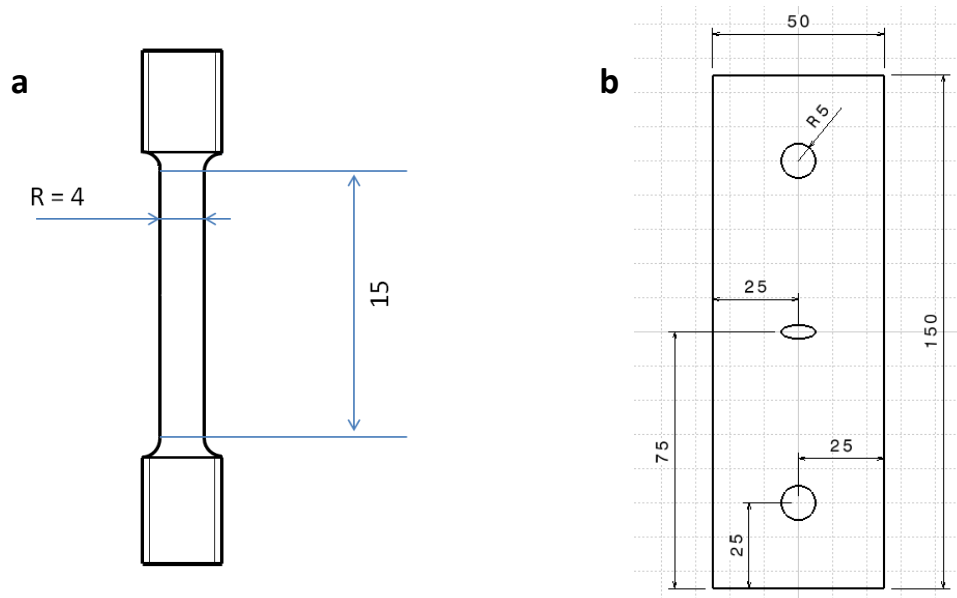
a) Schéma d’une éprouvette axisymétrique non-entaillée avec les dimensions de la zone utile en millimètres, b) Schéma d’une éprouvette CCT où les principales dimensions sont indiquées en millimètres
